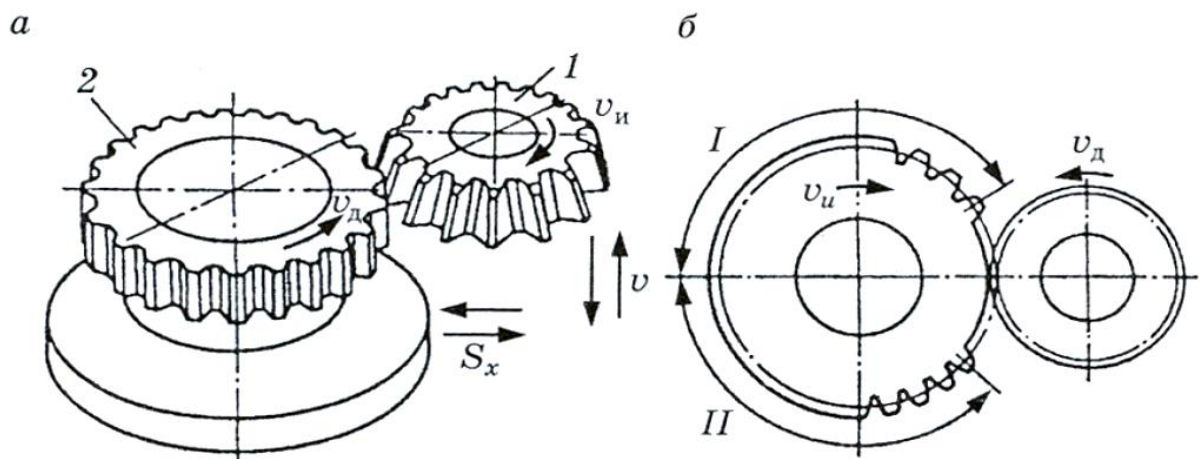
Схема нарезания зубьев зубодолблением круглым долбяком: 1 – долбяк; 2 – обрабатываемое зубчатое колесо
